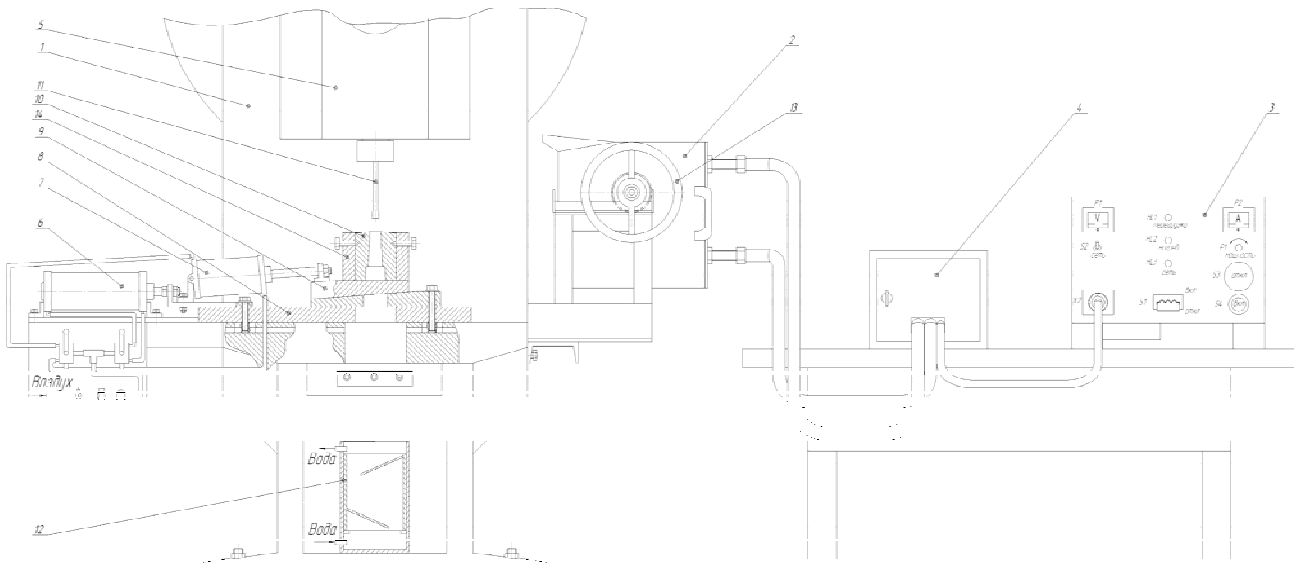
Установка для штамповки электродов контактной сварки: 1 – кривошипный пресс; 2 – разливочный узел; 3 – блок согласования; 4 – источник питания; 5 – молот; 6 – нижний пневмоцилиндр; 7 – верхний пневмоцилиндр; 8 – плита; 9 – клин; 10 – матрица; 11 – пуансон; 12 – охлаждаемая камера; 13 – рукоять; 14 – корпус
